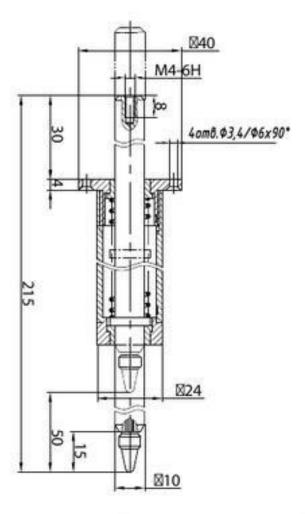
Габаритные и присоединительные размеры насадки Н(50)/С.
